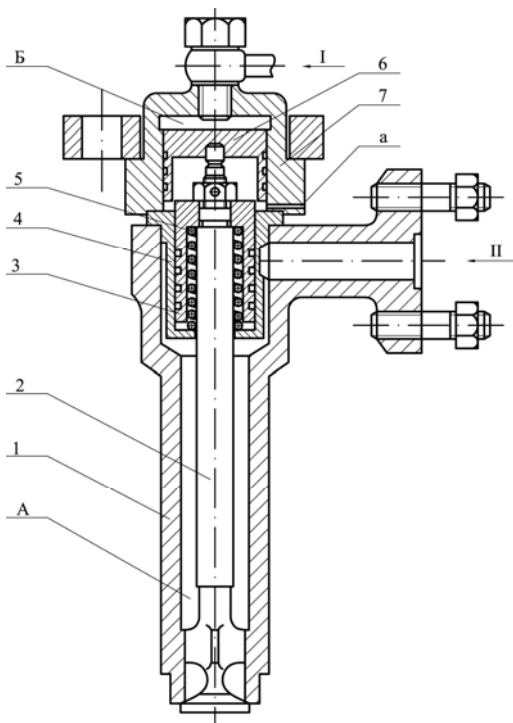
Пусковой клапан: 1 — корпус; 2 — клапан; 3, 6 — поршни; 4 — центrovочная втулка; 5 — пружина; 7 — колпак; А, Б — полости; а — отверстие; I — от воздухораспределителя; II — от баллона пускового воздуха
